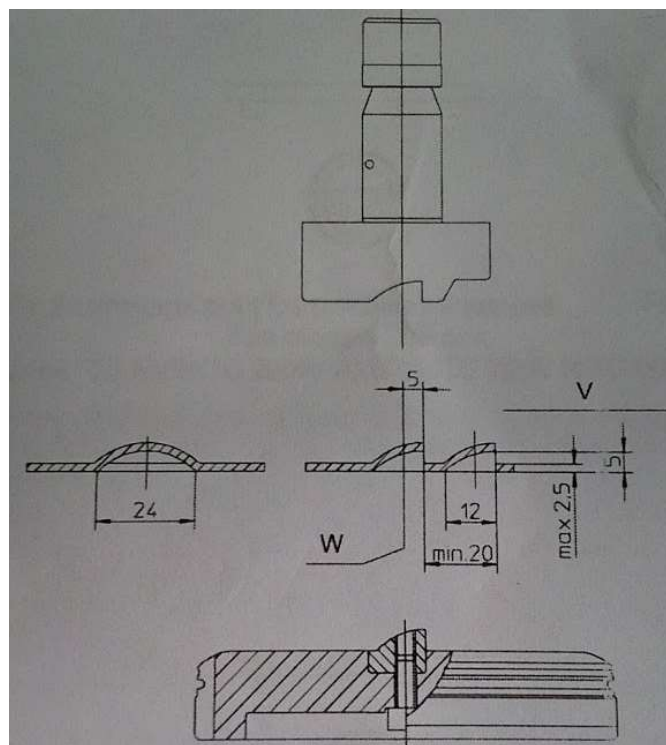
Desenho técnico das ferramentas para o fabrico de respiros.
